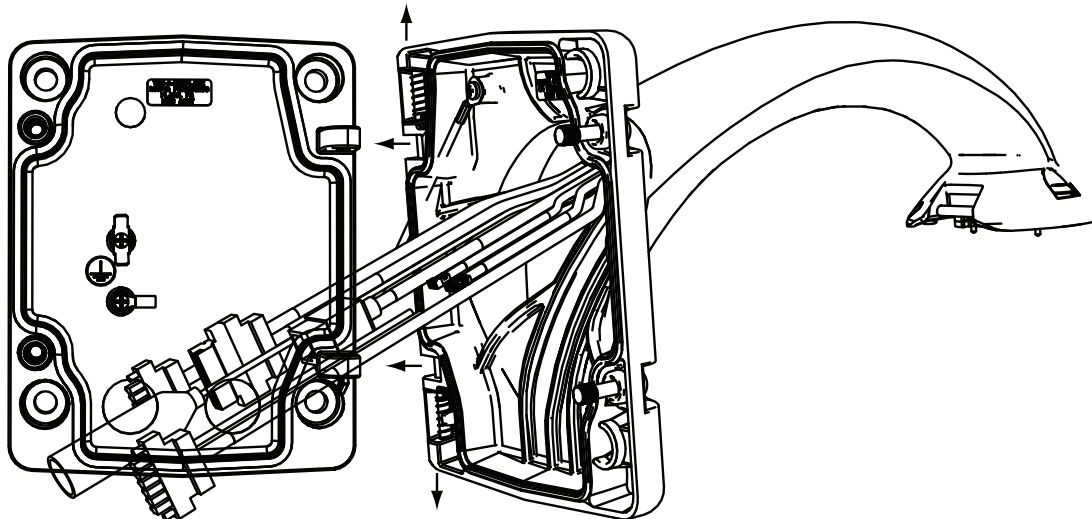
Подсоединение подвесного кронштейна к монтажной плате
